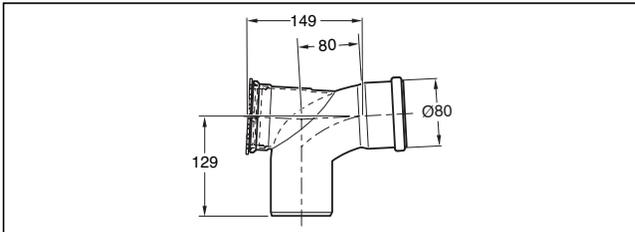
Bogen mit Prüföffnung lang (Maße in mm)
